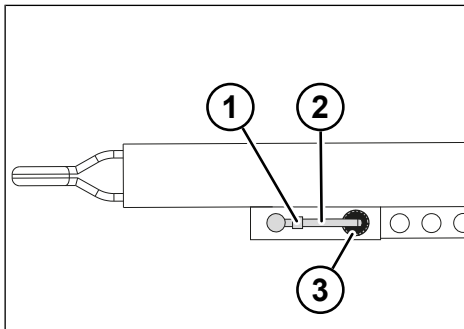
Регулирование длины с помощью приспособления быстрой регулировки
